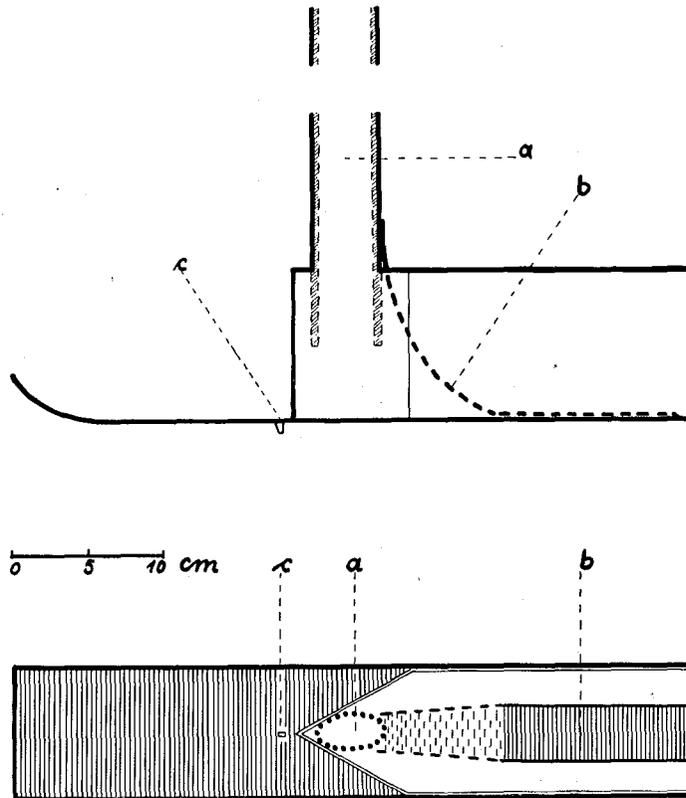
Drillkufe. Oben: Seitenansicht (schemat.); unten: Grundriß
